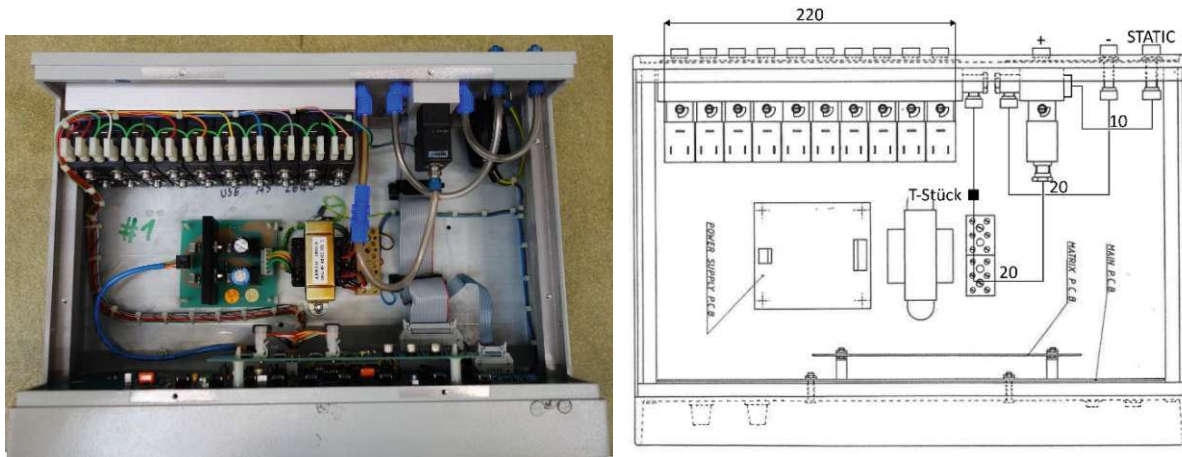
FCO 91, links geöffnet, rechts technische Zeichnung, aus [10]
